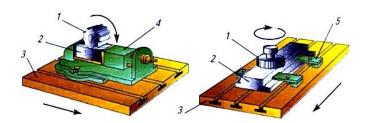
Фрезерование плоскостей: а — цилиндрической фрезой в тисках; 6 — торцевой фрезой на столе станка: 1 — фреза; 2 — заготовка; 3 — стол; 4 — тиски; 5 — прижим
